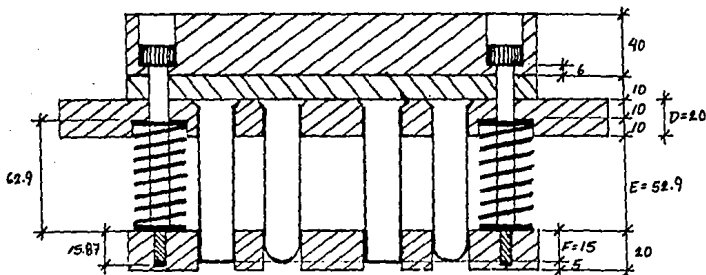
Parte superior del troquel modificada respecto a la figura 5.19, adaptándose a las dimensiones reales de los tornillos del prensachapas.
